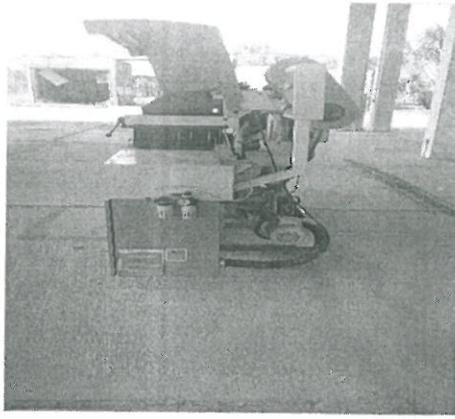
Tipos equipos de multilaminado en planta de segunda transformación
